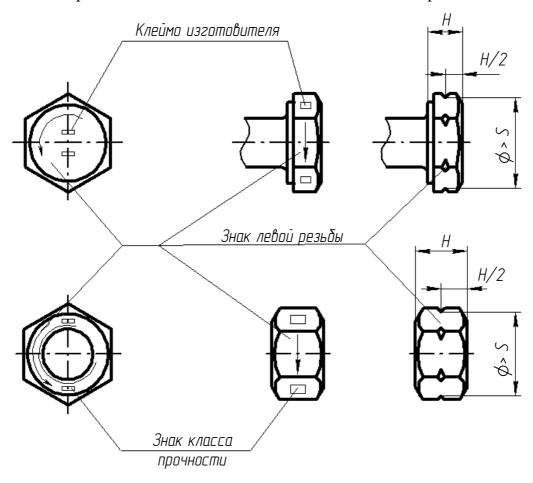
Нанесение знаков левой резьбы и клейма на головке болта, винта, гайки
